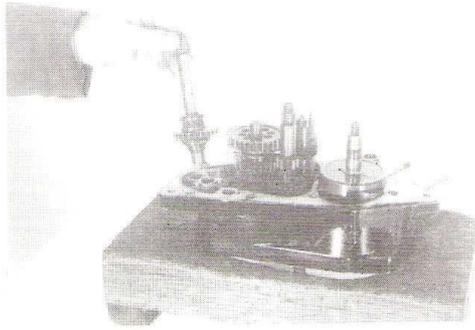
Empezaremos por desmontar manualmente el conjunto eje arranque.
